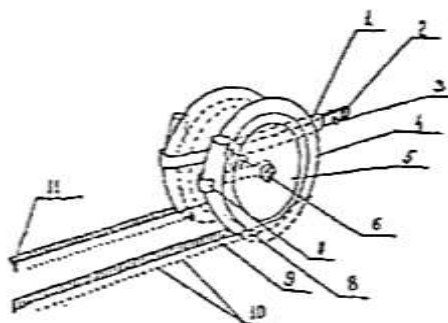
Технологический процесс работы двухдискового сошника с внешними ребрами-бороздкообразователями-уплотнителями: 1 – корпус; 2 – отверстие; 3 – болт; 4 – диск; 5 – реборда-бороздкообразователь-уплотнитель; 6 – ось; 7 – пластина; 8 – семянаправитель; 9 – бороздка; 10 – семена; 11 – щель
